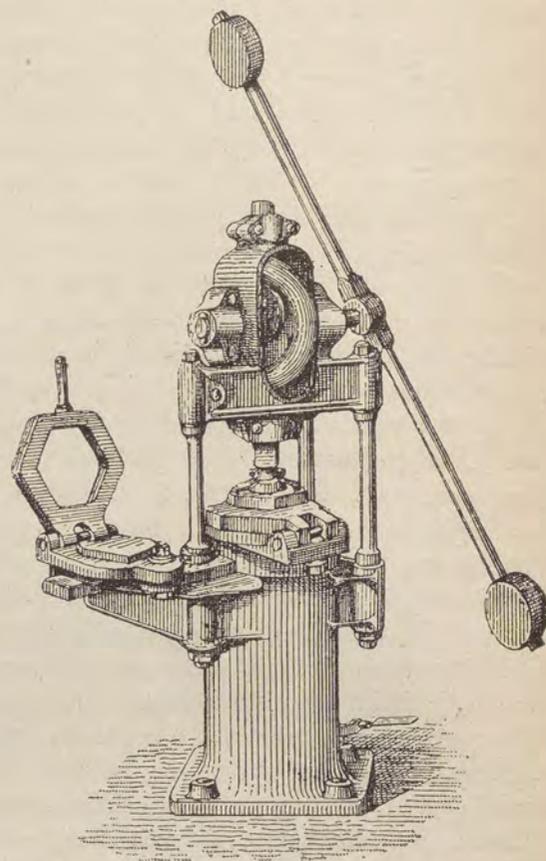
Lo strettoio a mano per quadrelle da pavimenti.
